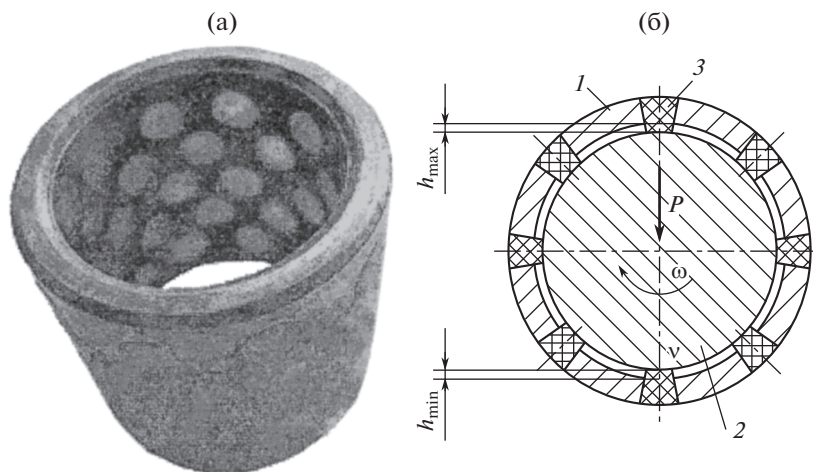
Полимерпорошковый подшипник (а) общий вид, (б) схема: 1 – порошковая матрица, 2 – вал, 3 – полимерные вставки.
